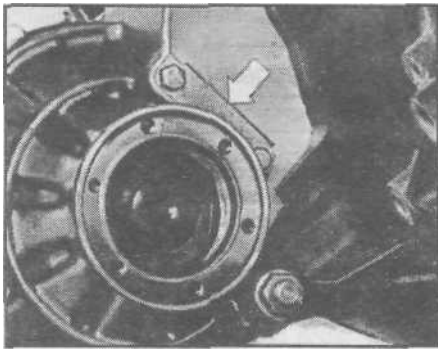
Снимите крышку с фланца ведущего вала (показана стрелкой)
